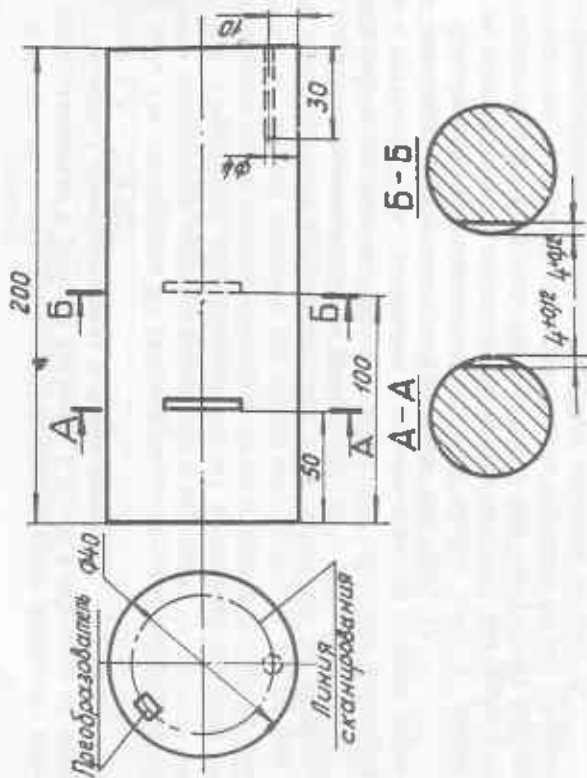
Столбчатый образец для настройки ультразвукового прибора при НК аляваторов
